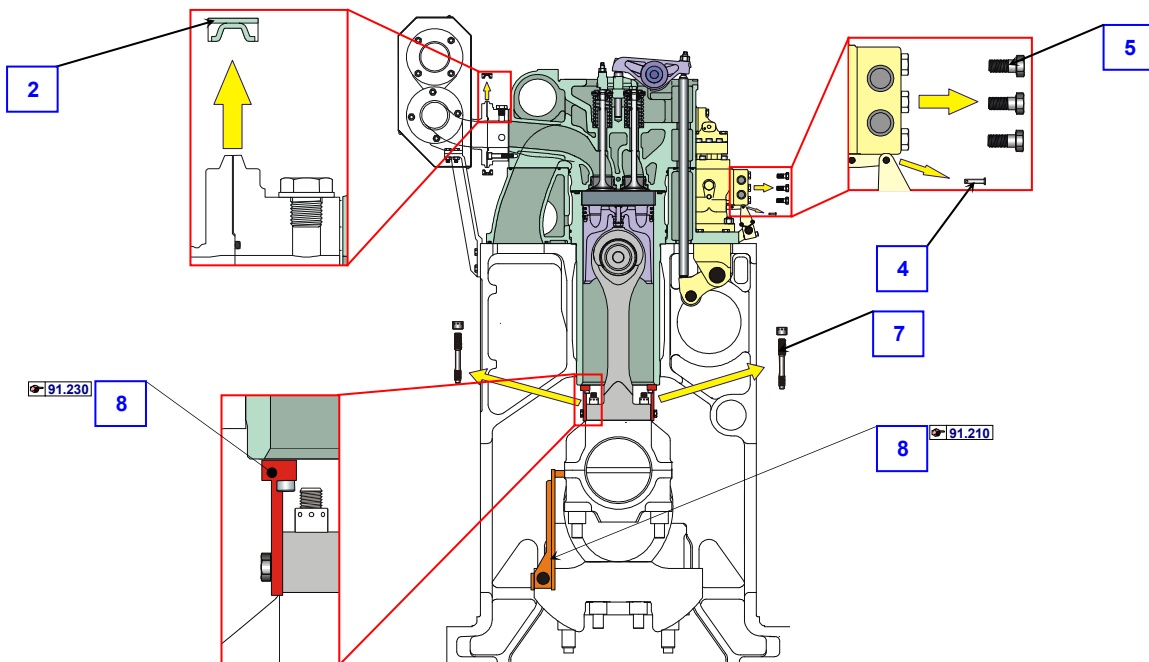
Mount support device & turning bracket (지지 장치 및 고정구의 설치)
